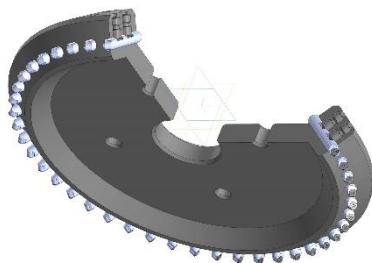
Торцева фреза зі стопорними додатковими гвинтами
